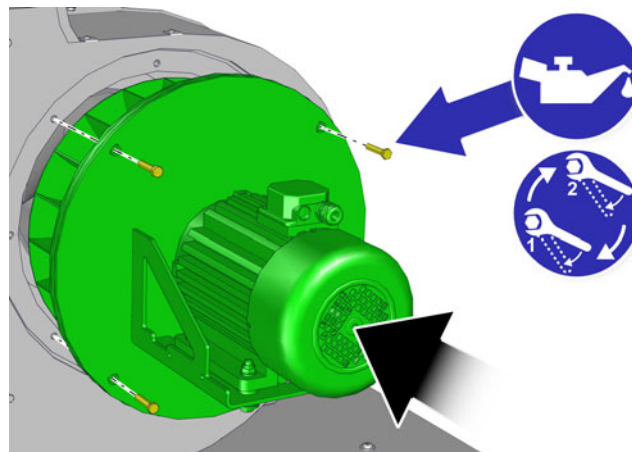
Nettoyage du rotor et remplacement du joint
